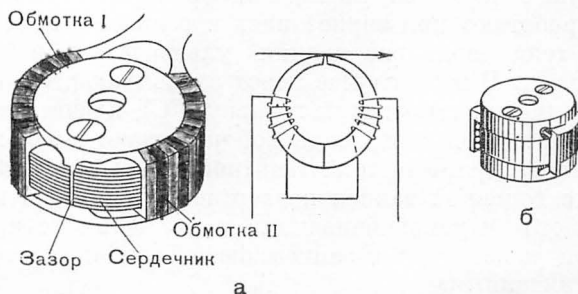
Конструкция (а) и общий вид (б) головки кольцевого типа
